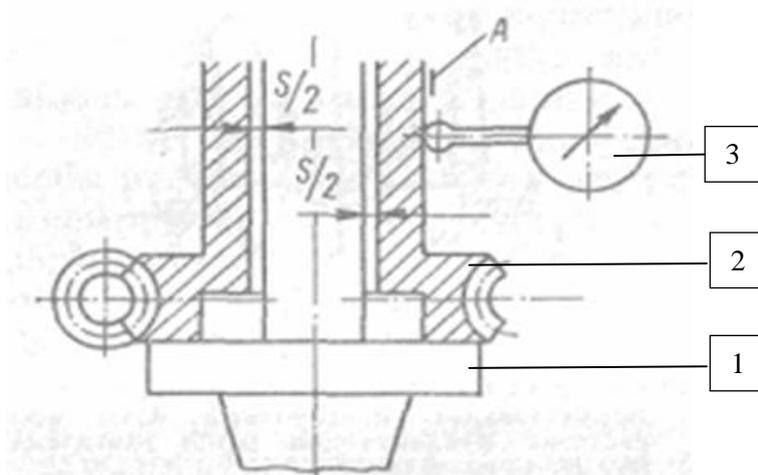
Установка червячного колеса по проверочной базе
